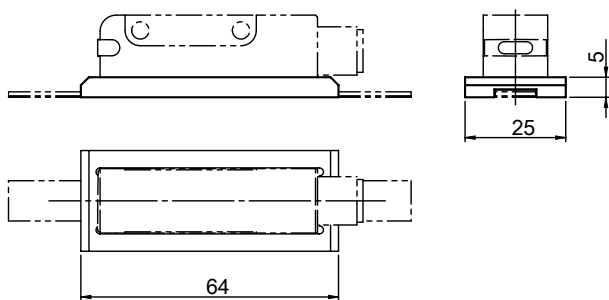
Guidage de capteur BAM TO-ML-019-SL1
